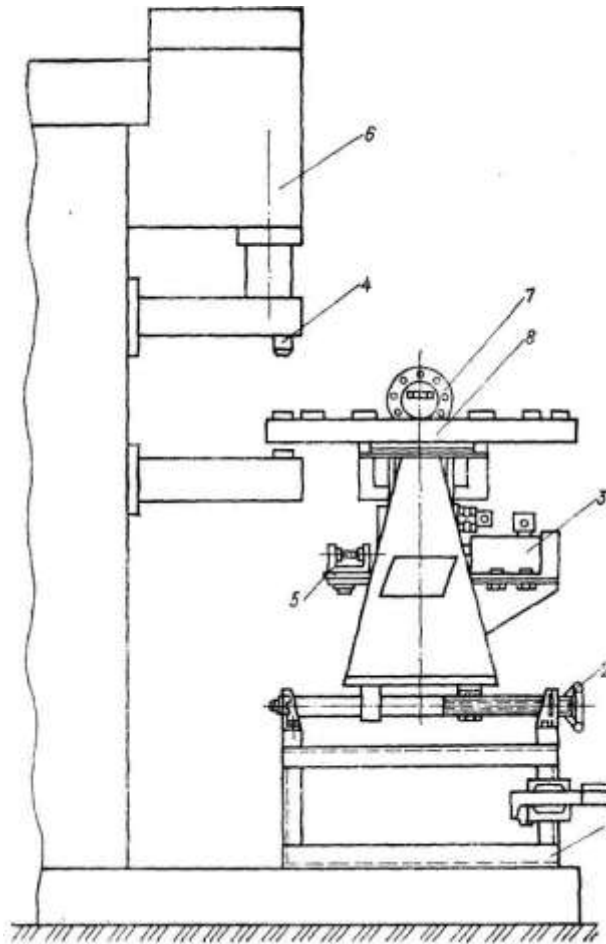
Установка для контактной сварки с многопозиционным поворотным столом
